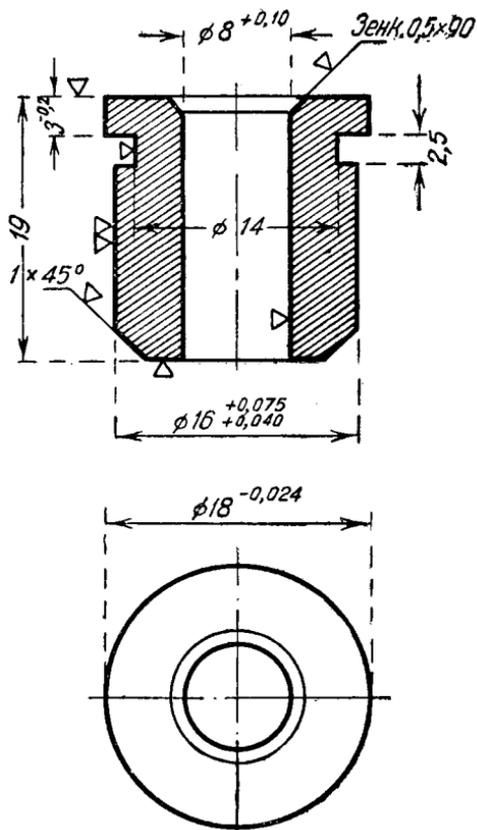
Дет. 07-33. Втулка к корпусу тяги дросселя
